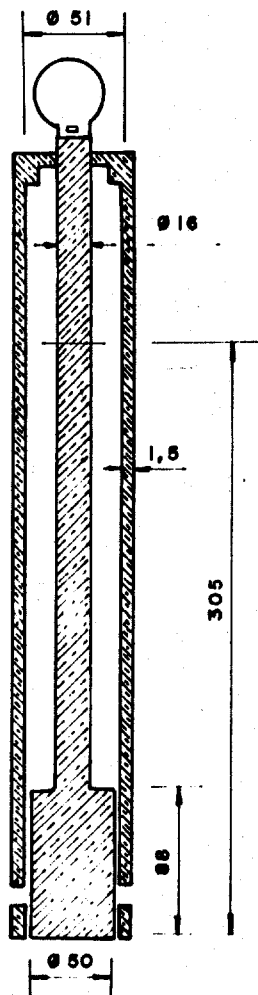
DIMENSÕES DO SOQUETE METÁLICO
